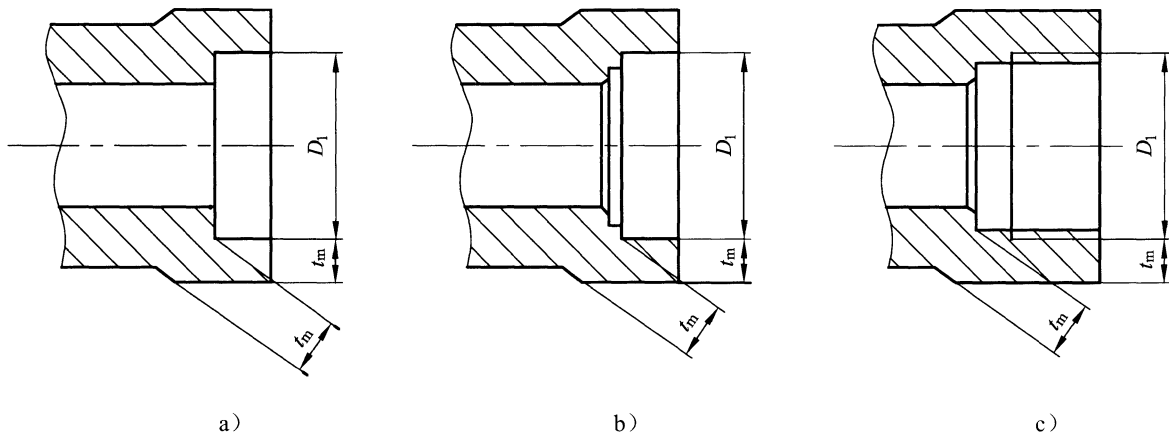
承插焊接端、螺纹连接端的尺寸
